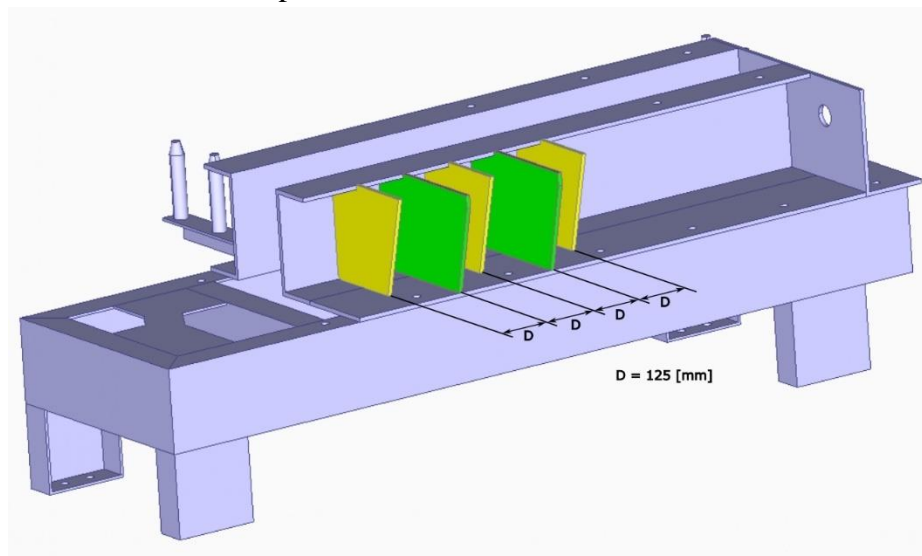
Posición de placas de refuerzo. Fuente: Elaboración propia.
